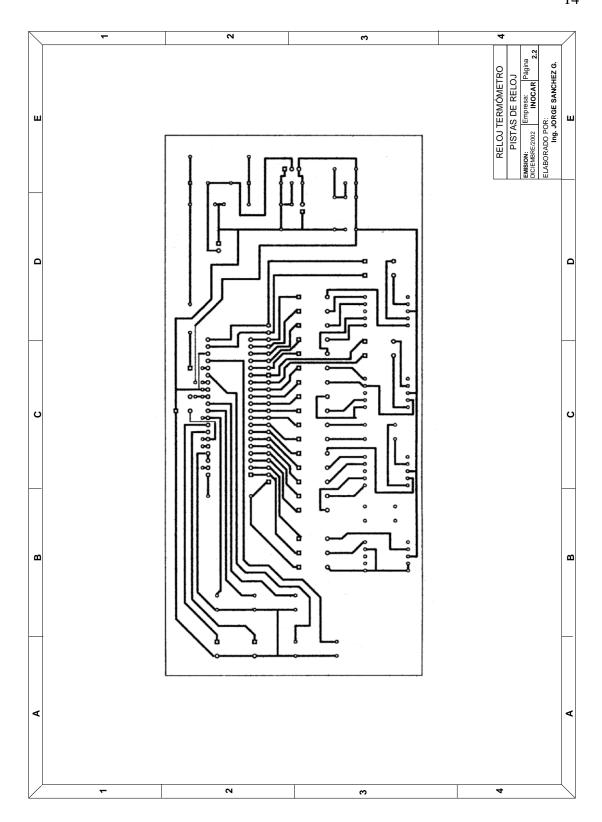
Tarjeta de reloj (diagrama de pistas lado de soldadura)
